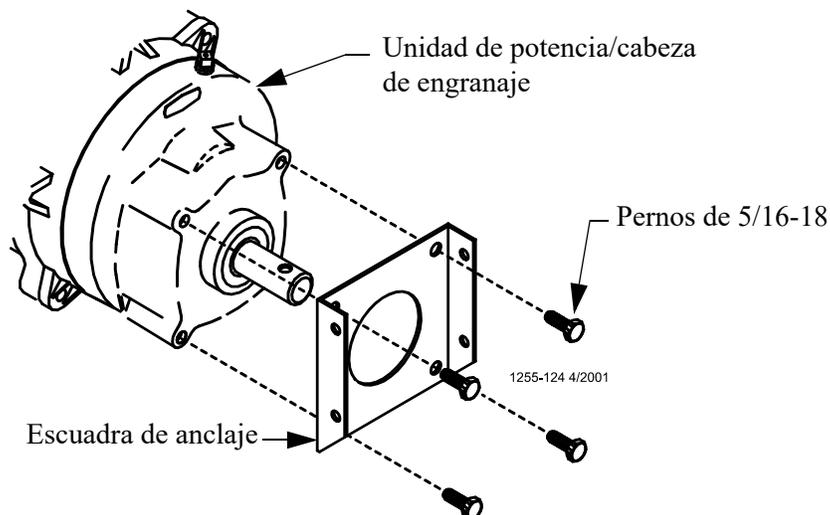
Instalación del soporte de anclaje en la unidad de potencia/cabeza de engranaje
